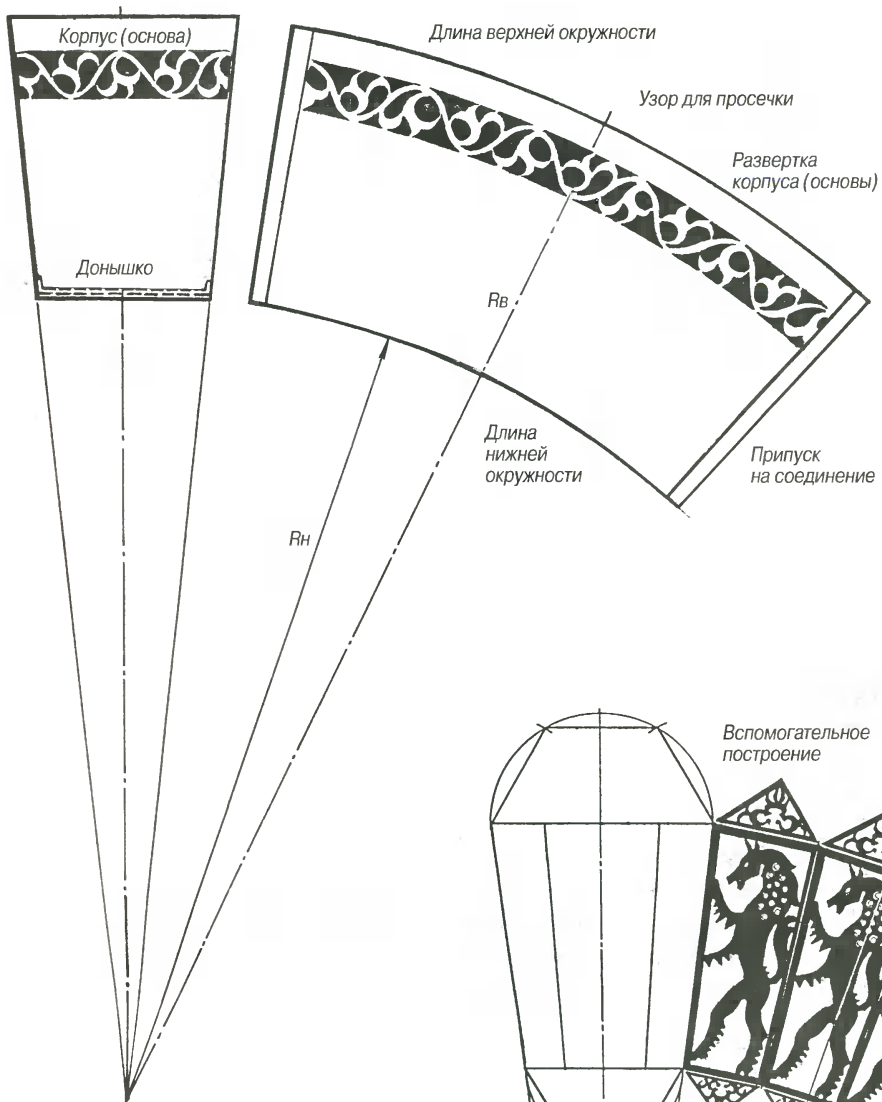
Построение развертки корпуса (основы) карандашницы.
